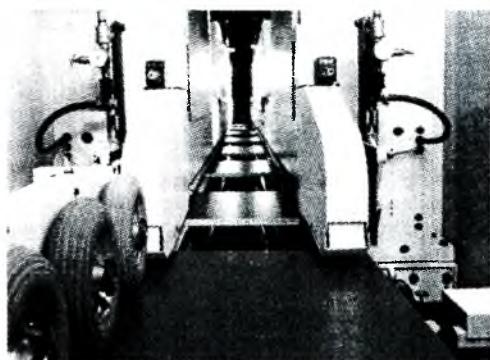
Двухсторонний кромкооблицовочный станок фирмы "Хомаг"
